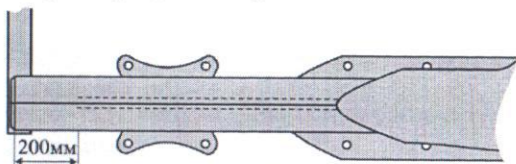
Контроль околошовной зоны сварного соединения на верхних стенках продольных балок рамы
